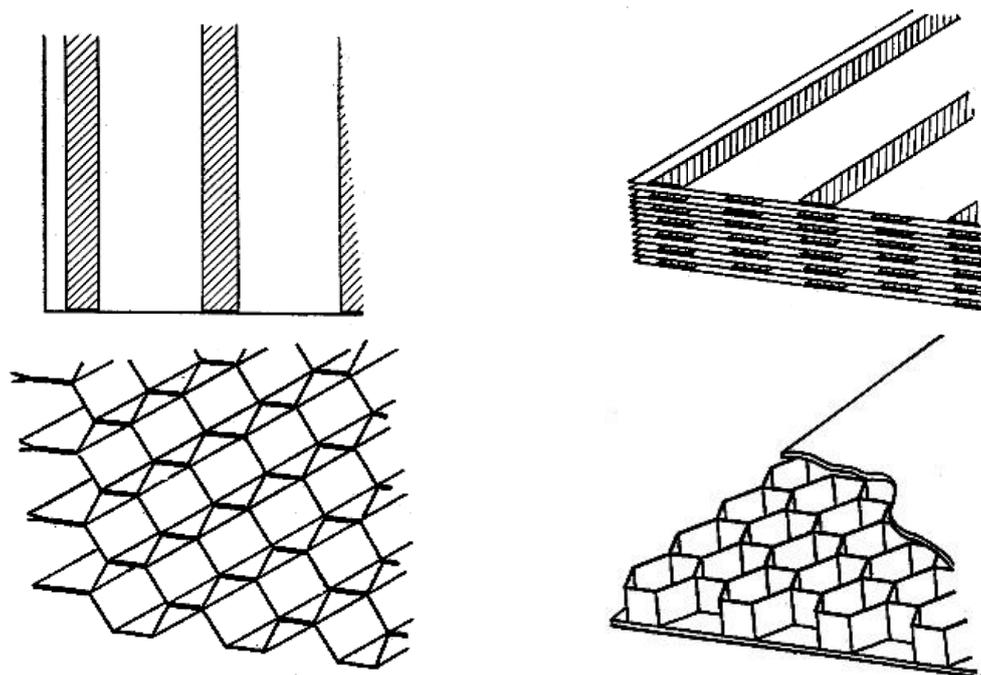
17. Этапы изготовления сотовой конструкции фюзеляжа самолета
